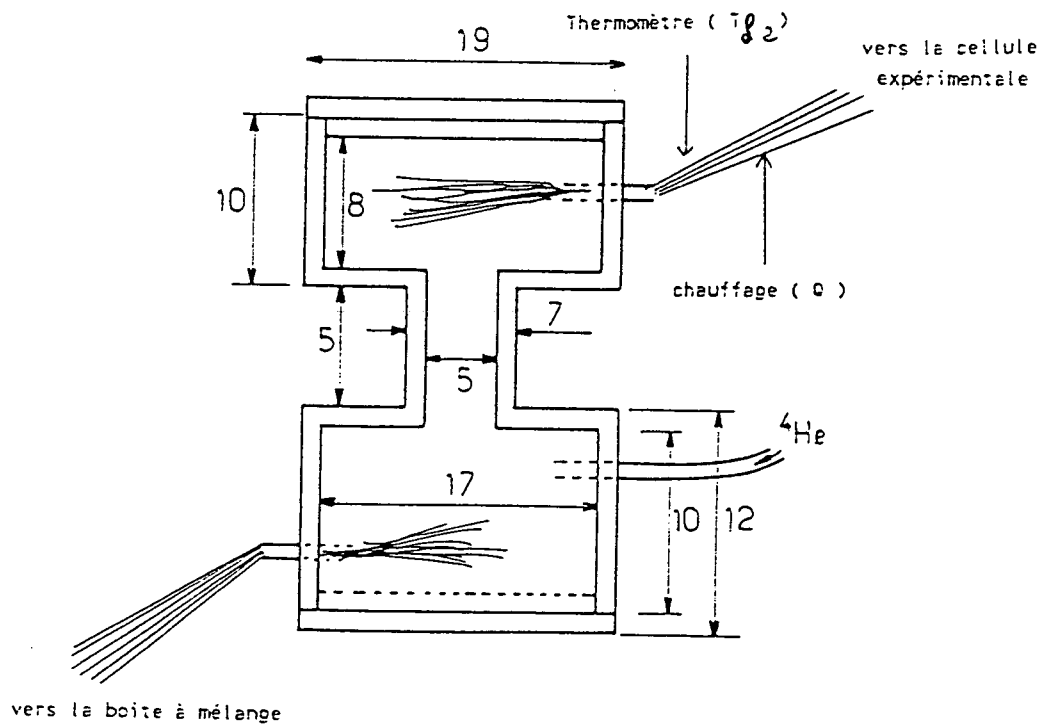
Dimensions de l'interrupteur thermique (mm).
